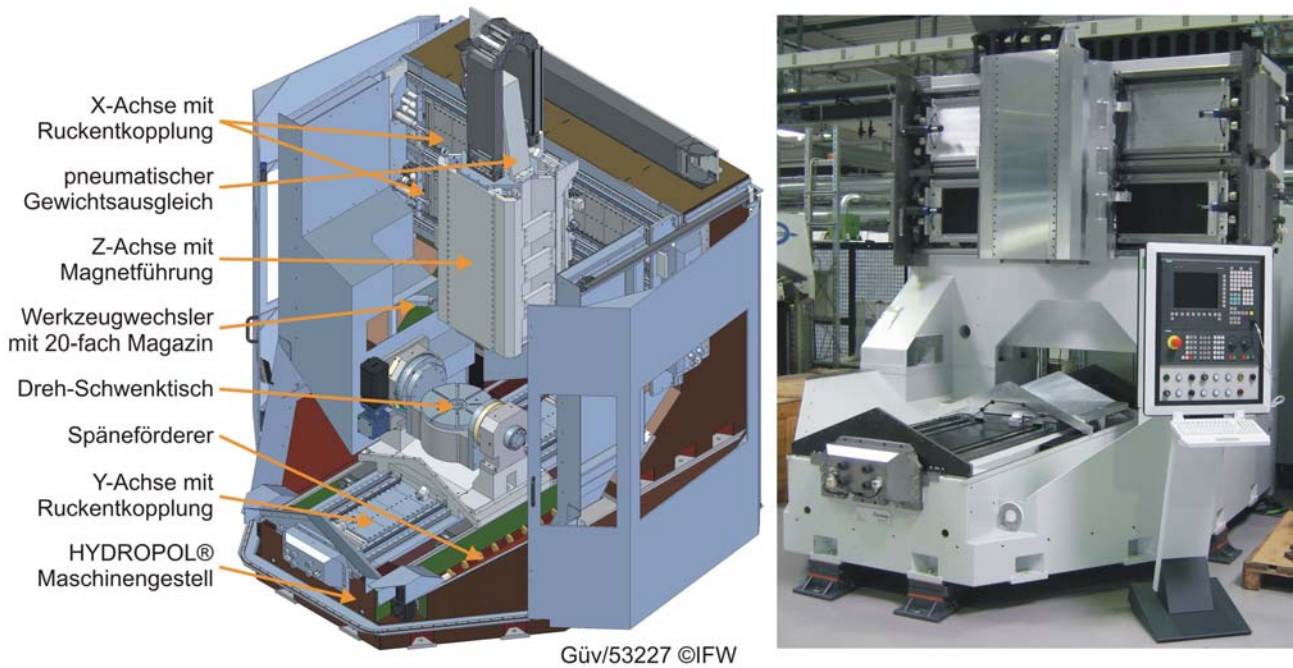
CAD-Modell und aktueller Stand des Werkzeugmaschinenprototyps
